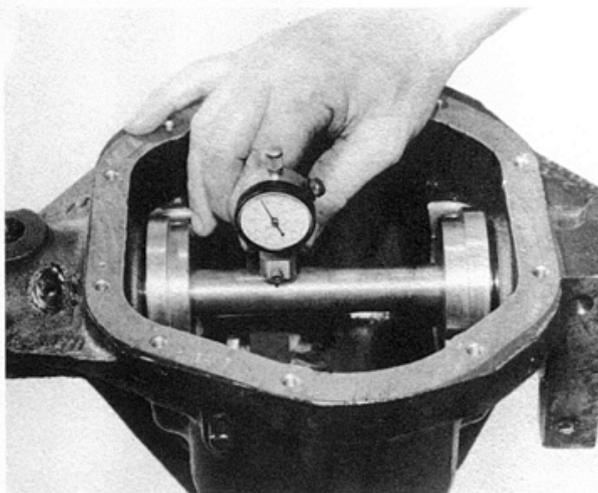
Com o dispositivo instalado verificar a profundidade do pinhão.
